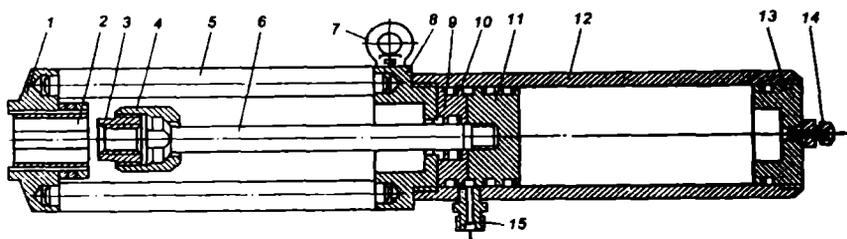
Гидродомкрат СМЖ-82А для натяжения арматуры:
